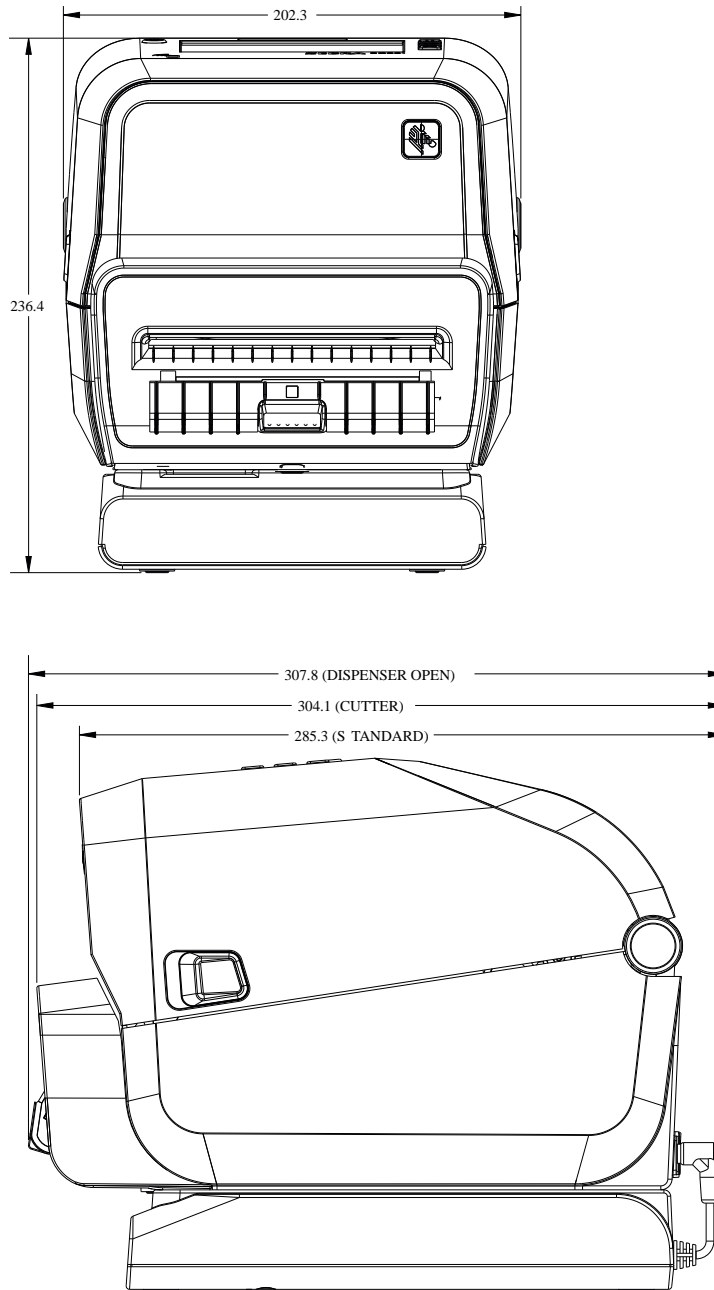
Modelos de transferência térmica ZD421/ZD621 – dimensões para impressora com a opção Cutter (Cortador) instalada
